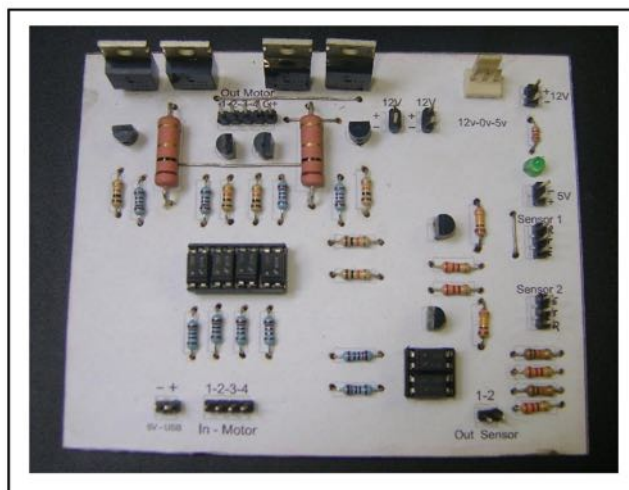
Placa Eletrônica para controle do motor de passo e sensores infravermelho
